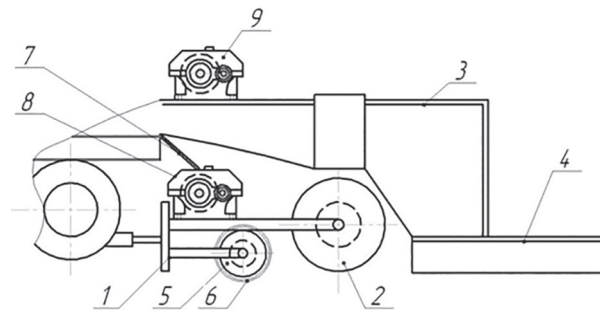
Конструктивно-технологическая схема катка-ложеобразователя машины для уборки лука
